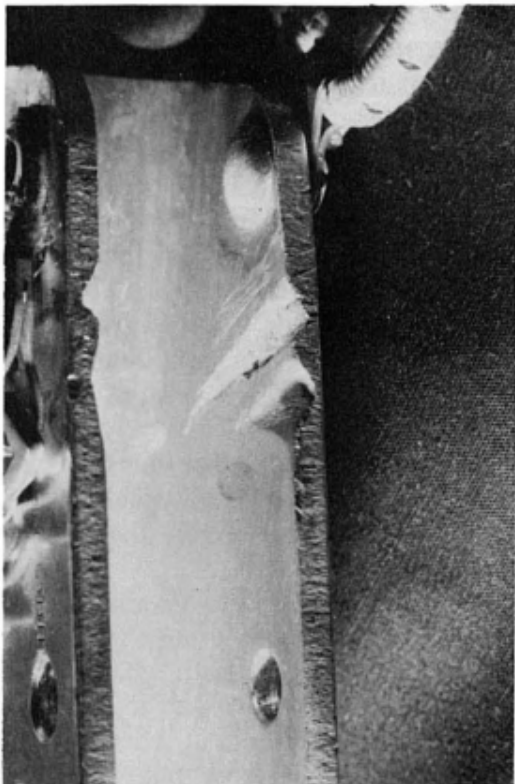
Крупный план пазов, пропиленных под спусковой механизм, и зазора под шнур.
